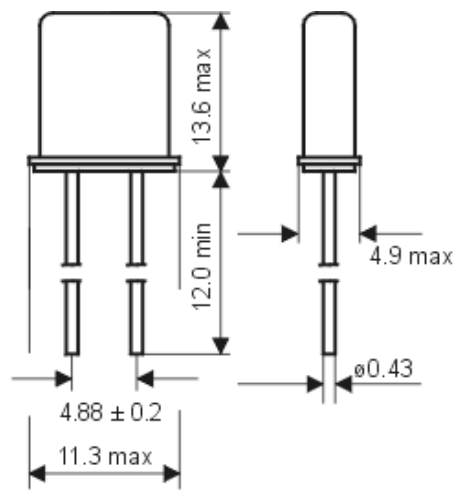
Габаритні розміри кварцового резонатора HC-49S
